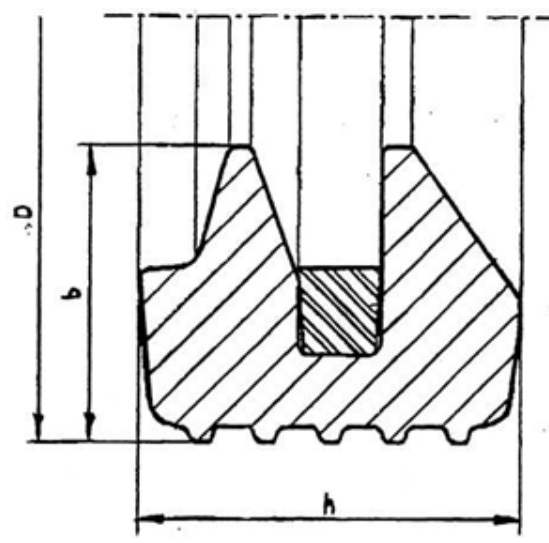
Уплотнительного кольца двухлепесткового типа
